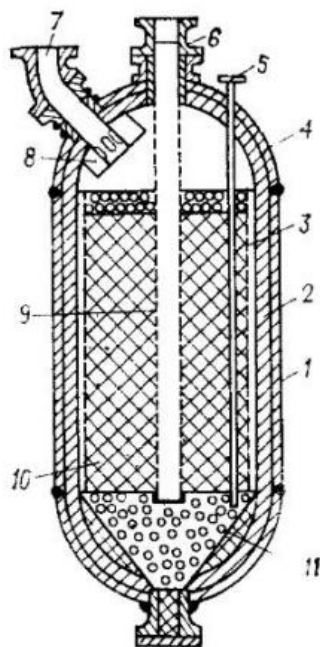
Реактор риформинга с радиальным вводом газосырьевой смеси [1]: 1 – корпус; 2 – футеровка; 3 – перфорированный стакан с сеткой; 4 – днище; 5 – штуцер для термопары; 6 – штуцер для вывода газо-продуктовой смеси; 7 – штуцер для ввода газо-сырьевой смеси; 8 – распределитель; 9 – перфорированная труба с сеткой; 10 – катализатор; 11 – фарфоровые шары
